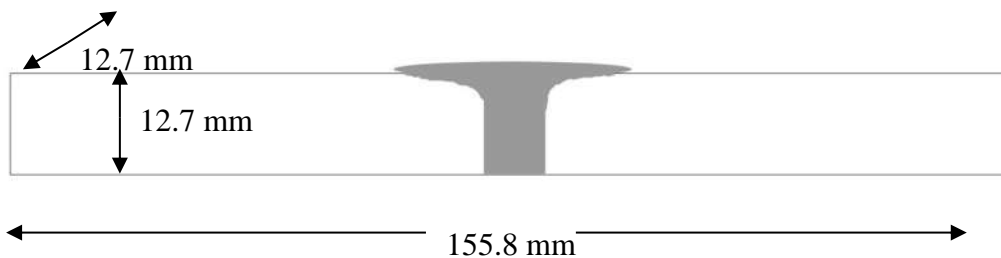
Dimensiones del corte realizado a las placas unidas por soldadura.
